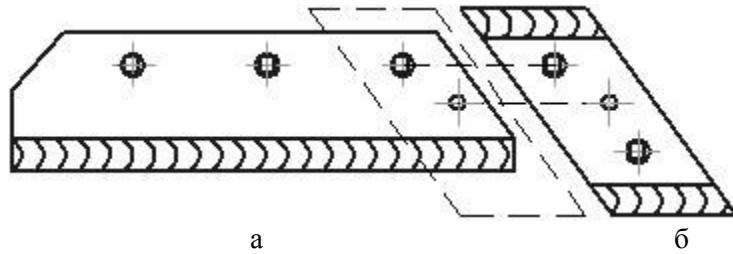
Лемех плужный П-702 МД модернизированный с обратным долотом:
